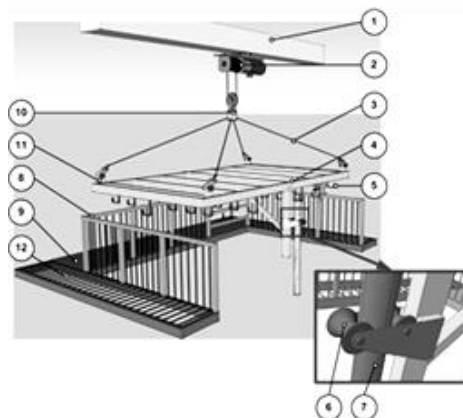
Трехмерная модель устройства для подъема пожарных рукавов в башенную сушилку №4: 1 – Железобетонная балка; 2 – электрелебедка; 3 – стропа; 4 – рама; 5 – крюк; 6 – упорный ролик; 7 – направляющая; 8 – перила; 9 – рабочая площадка; 10 – подвижный блок; 11 – вертлюг; 12 – боковая площадка
